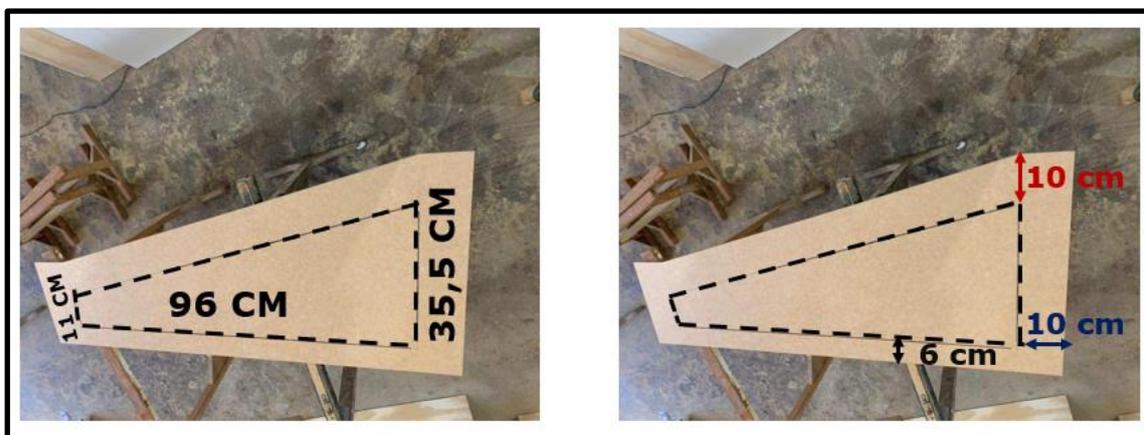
Face lateral da rampa reta com trapézio traçado para recorte.
